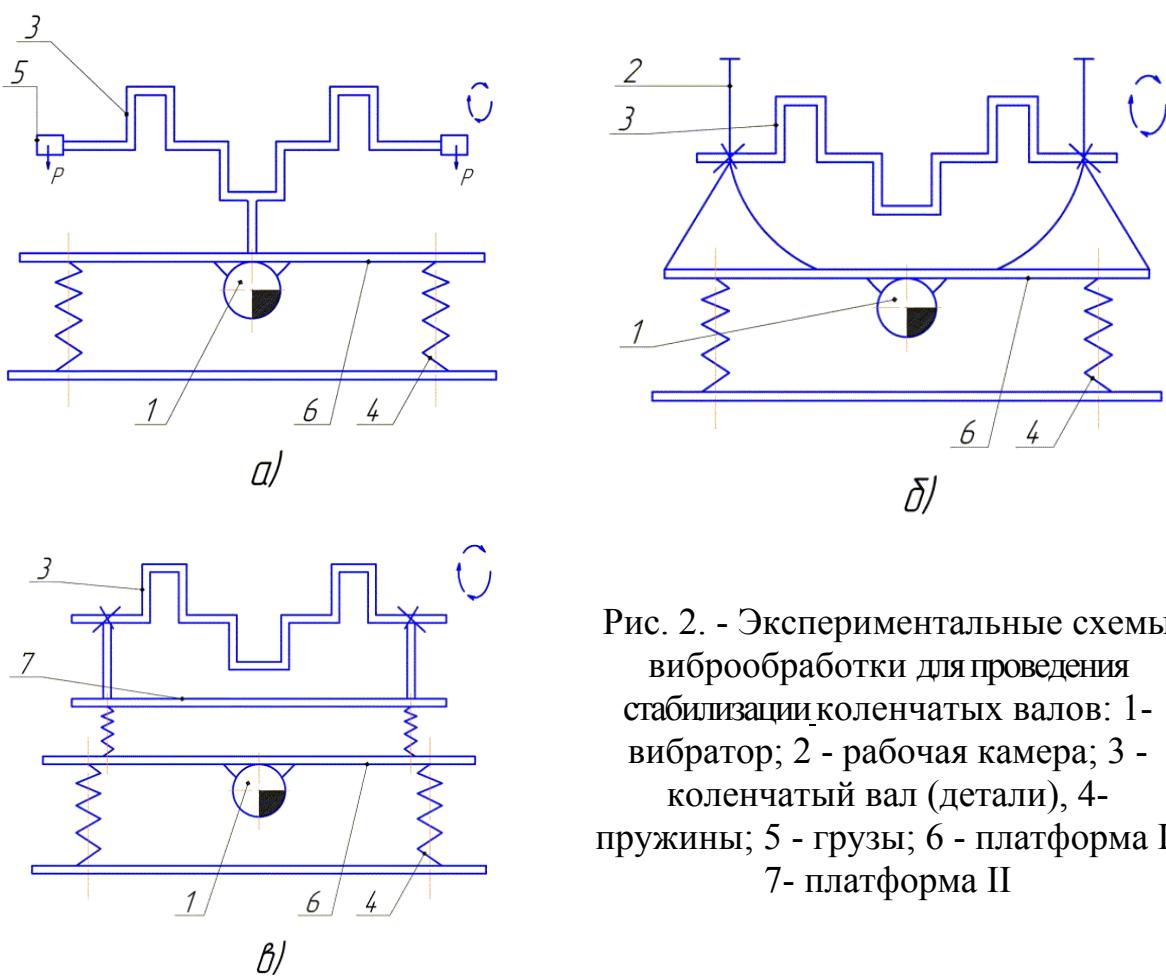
Экспериментальные схемы виброобработки для проведения стабилизации коленчатых валов: 1-вибратор; 2 - рабочая камера; 3 - коленчатый вал (детали); 4-пружины; 5 - грузы; 6 - платформа I; 7- платформа II
